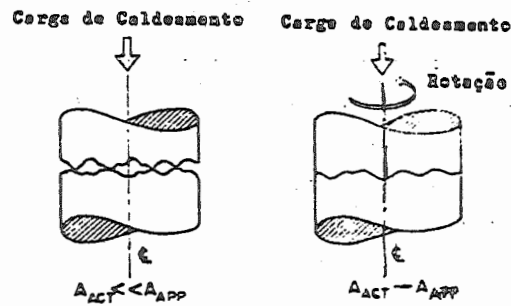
Efeito da rotação no mecanismo da soldagem por atrito
